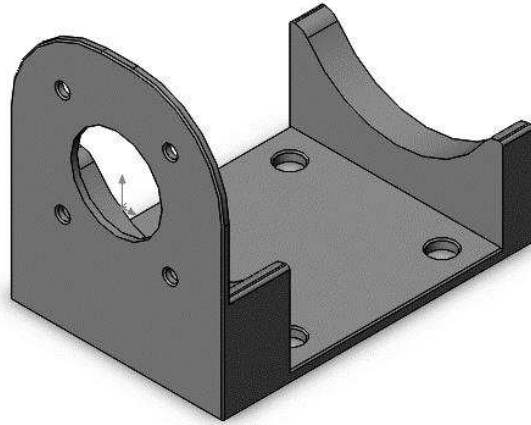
Крепление для энкодера ППК-15 (вид 1)
